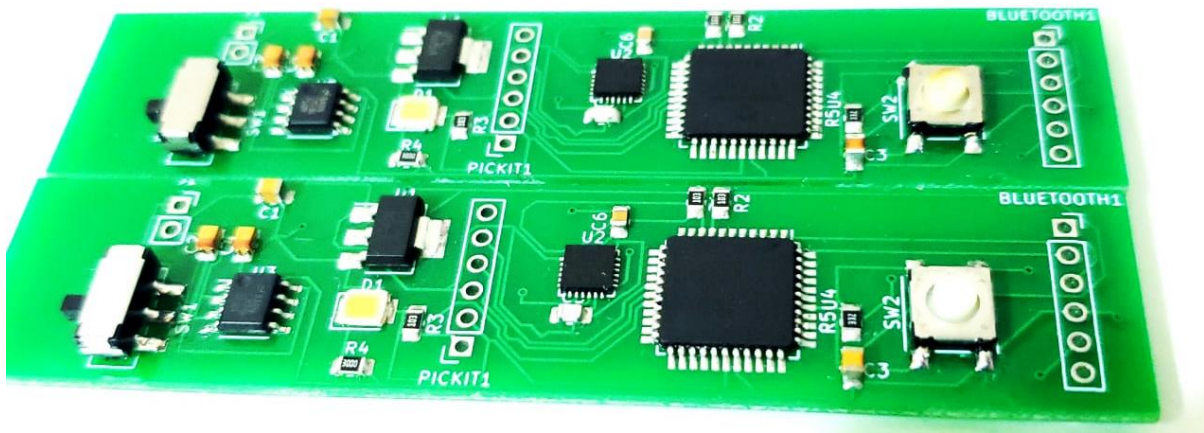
TARJETA DE CIRCUITO IMPRESO ENSAMBLADA
